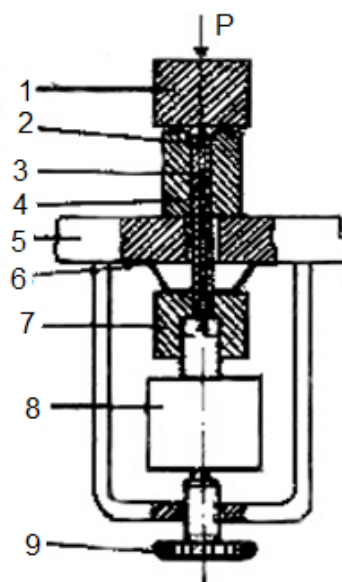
Схема прибора для измерения контактной деформации
